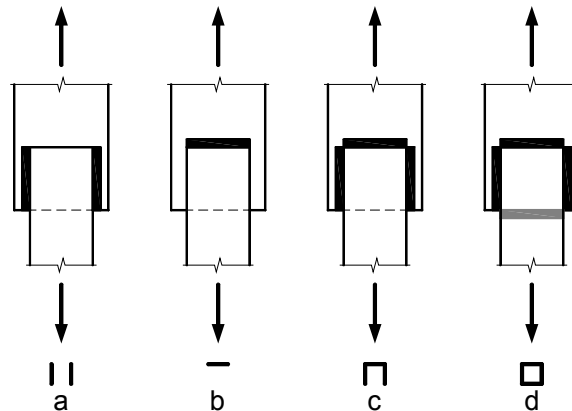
Schweißnahtgeometrie der Versuchskörper nach [45]
